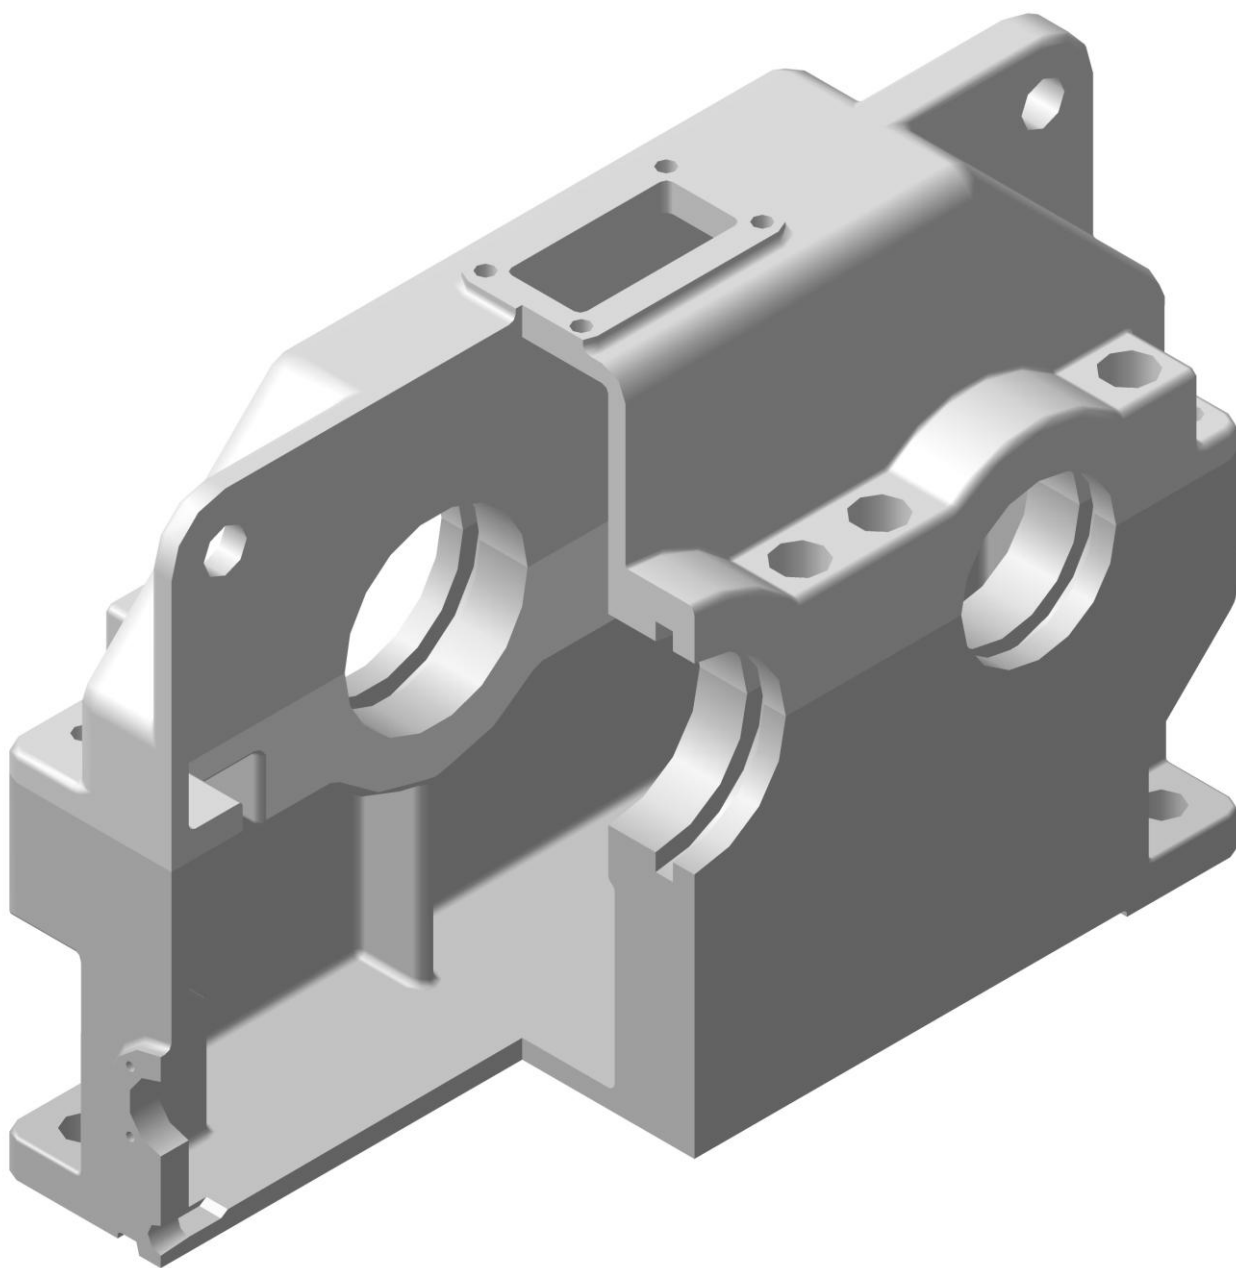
(лист 3, листов 3) Конструкции корпусных деталей цилиндрических редукторов с внутренним расположением подшипниковых бобышек
